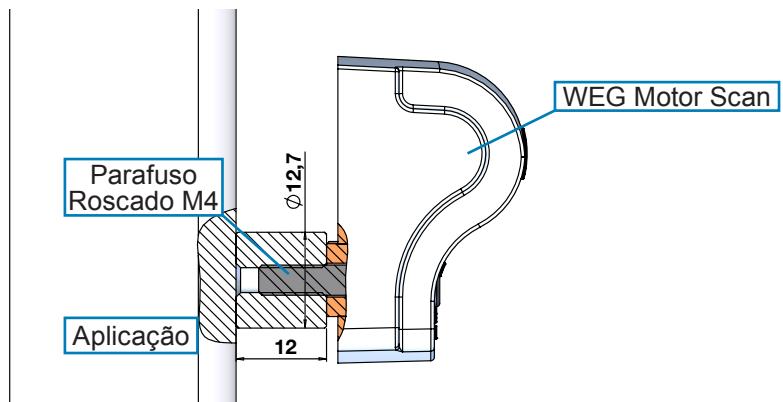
Detalhe da fixação do sensor em outros ativos
